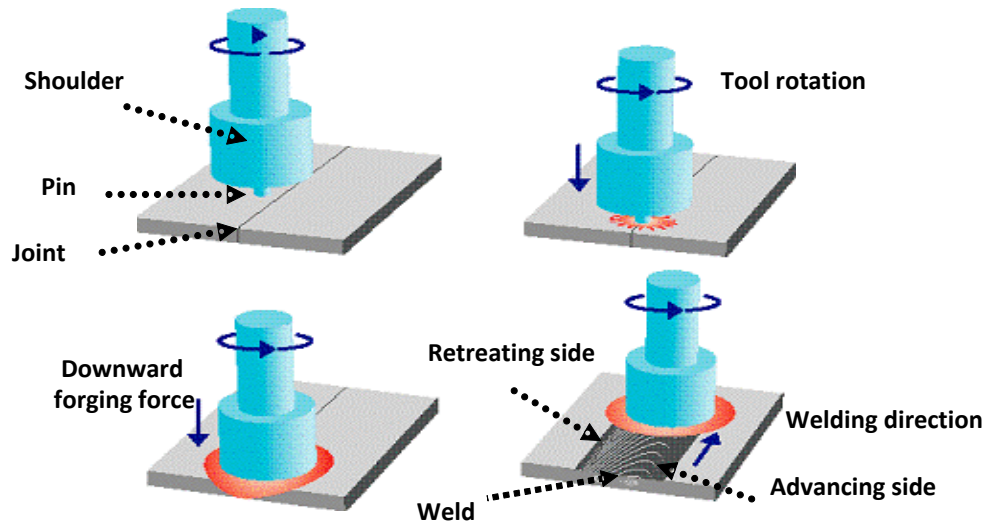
Principe du procédé de soudage FSW [Posada 2003, Aissani 2010a].
